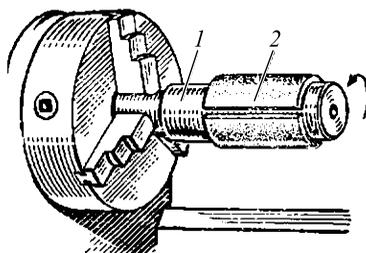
Инструмент для притирки отверстий на токарном станке
